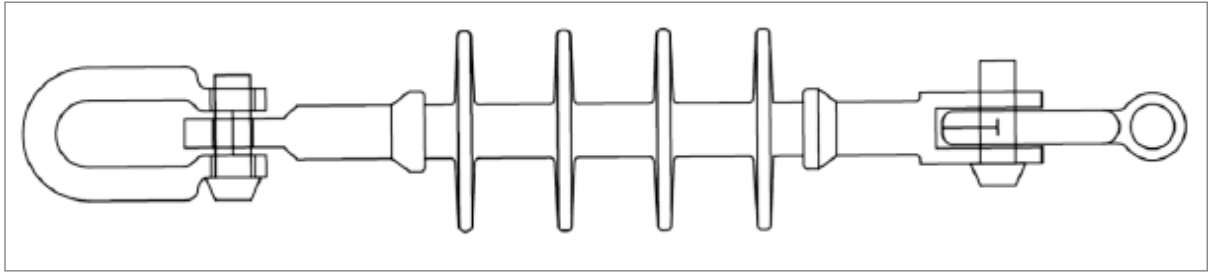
Esquema del modelo de aislador de retención polimérico elegido.
